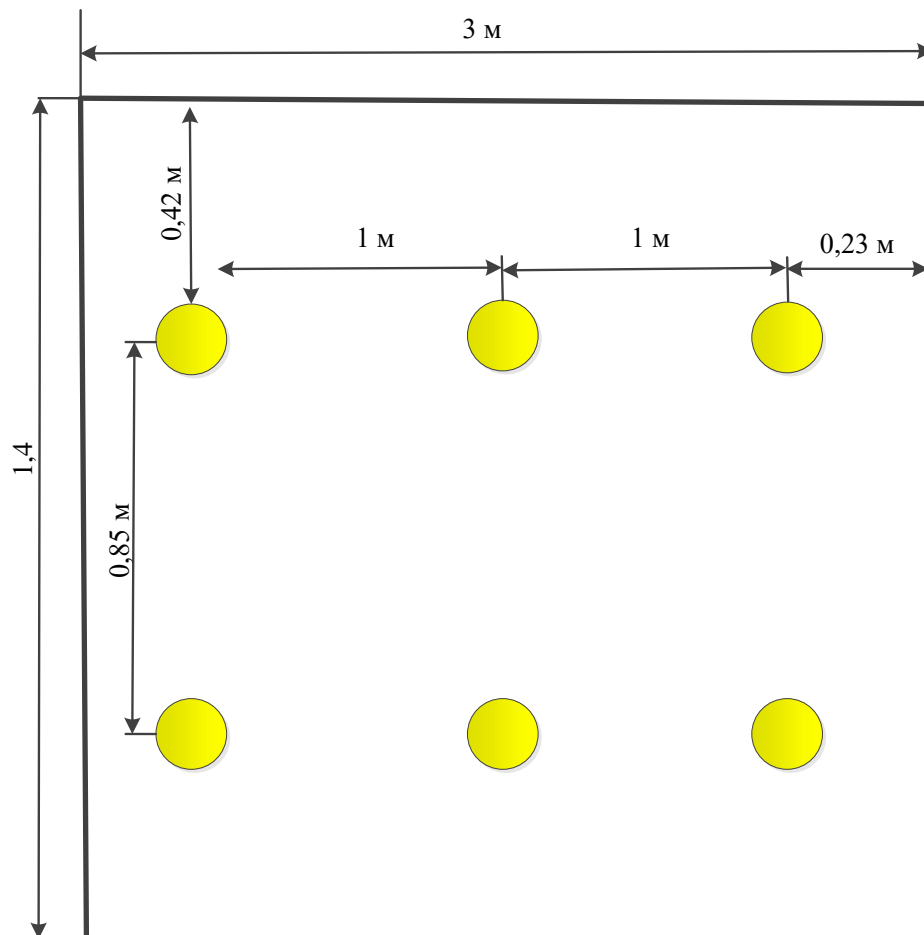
План размещения светодиодных ламп в салоне электро-мобиля
